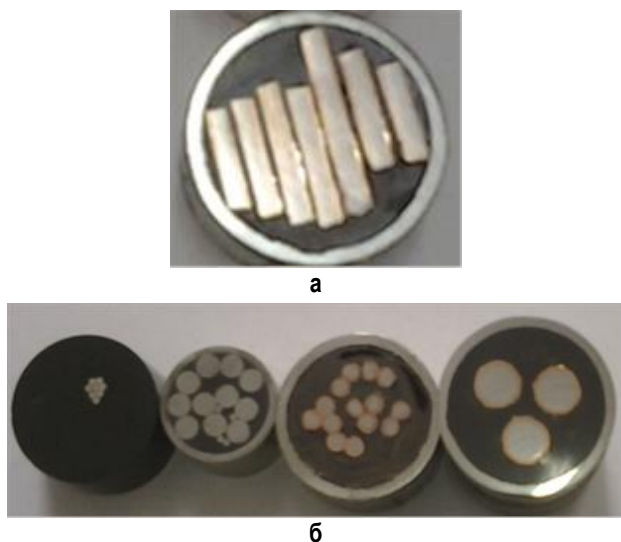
Вид образцов для измерения шероховатостей сердечника и оболочки: а – в продольном сечении, б – в поперечном сечении
